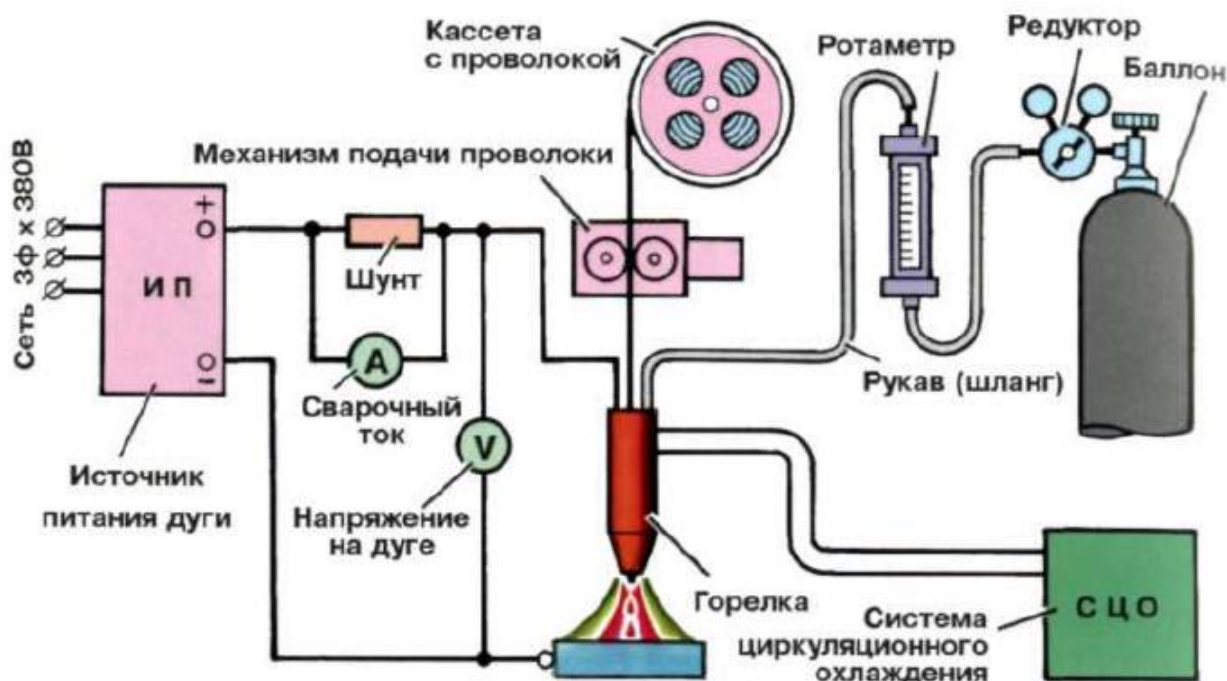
Сварка плавящимся электродом в защитных газах
